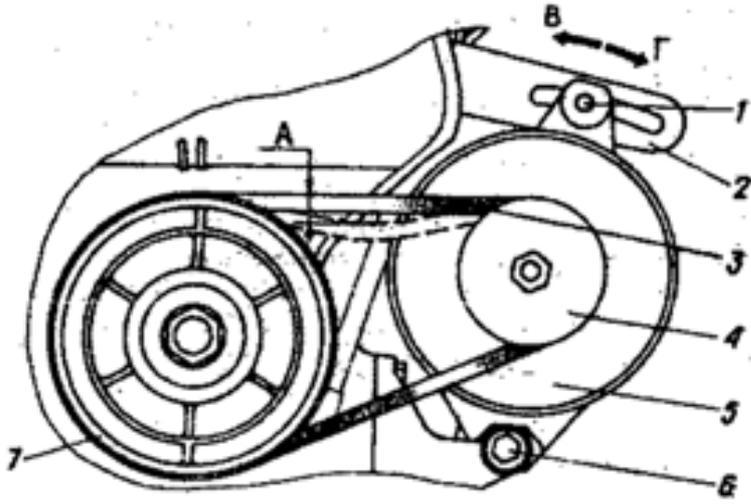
Привод генератора и проверка натяжения ремня: 1 - болт крепления генератора к натяжной планке; 2 - планка натяжная; 3 - ремень; 4 - шкив привода генератора; 5 - генератор; 6 - болт крепления генератора к кронштейну; 7 - шкив коленчатого вала.
